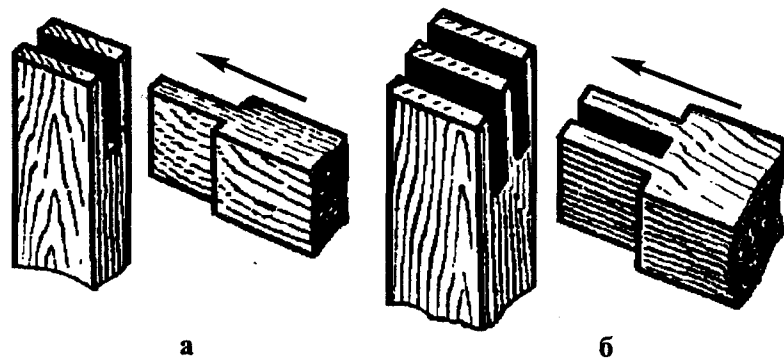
Шиповое соединение деталей: а — одинарным шипом; б — двойным шипом
